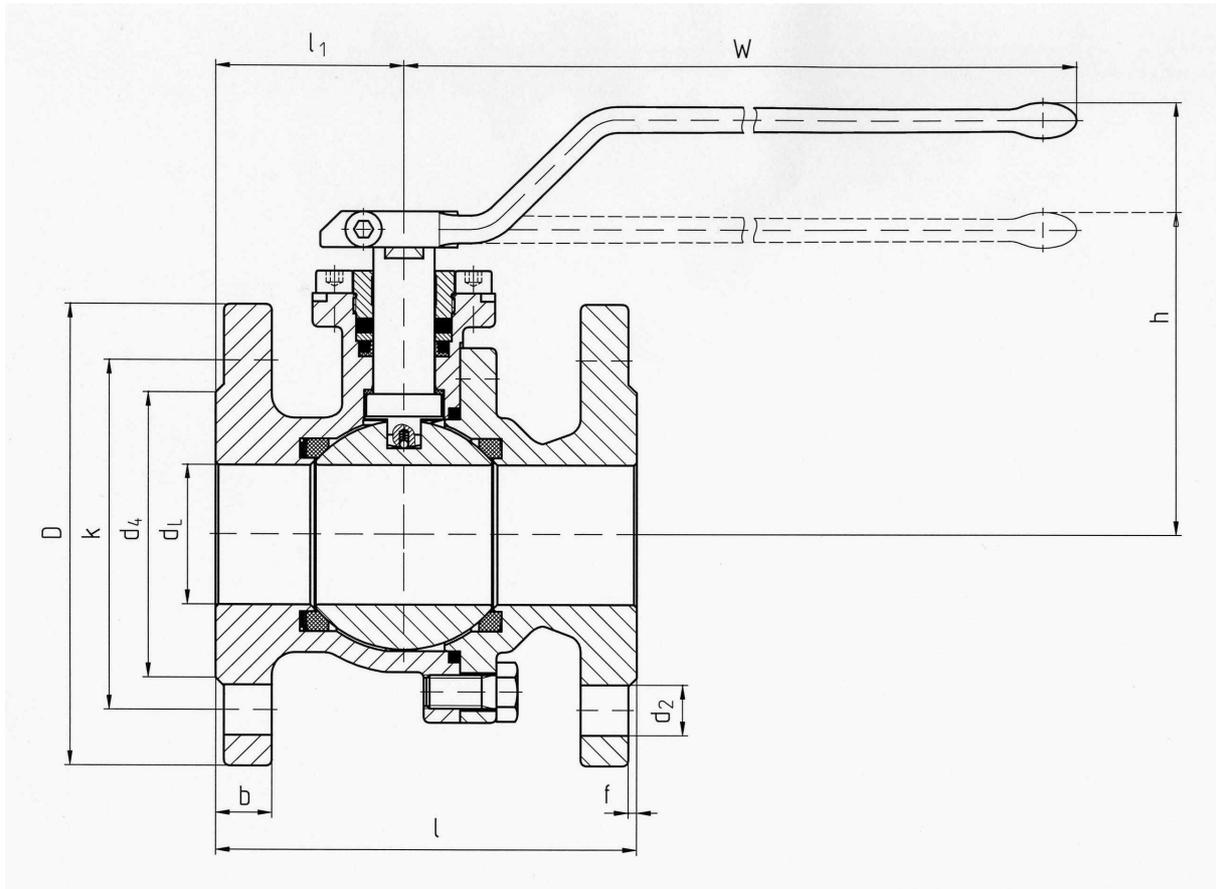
Kugelhahn mit Flanschanschluss nach DIN EN 1092-1 Form B1; Baulänge Grundreihe 27 (kurz) nach EN 558-1 (F18 nach DIN 3202 Teil 1)
